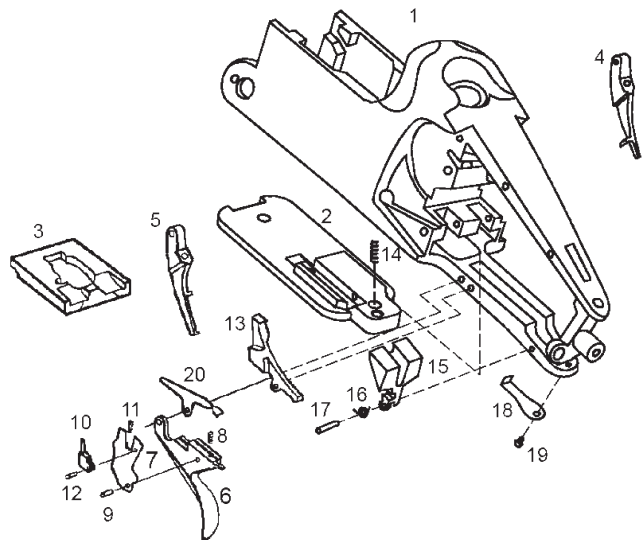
Детали ружей MP-27М-1С и MP-27ЕМ-1С
